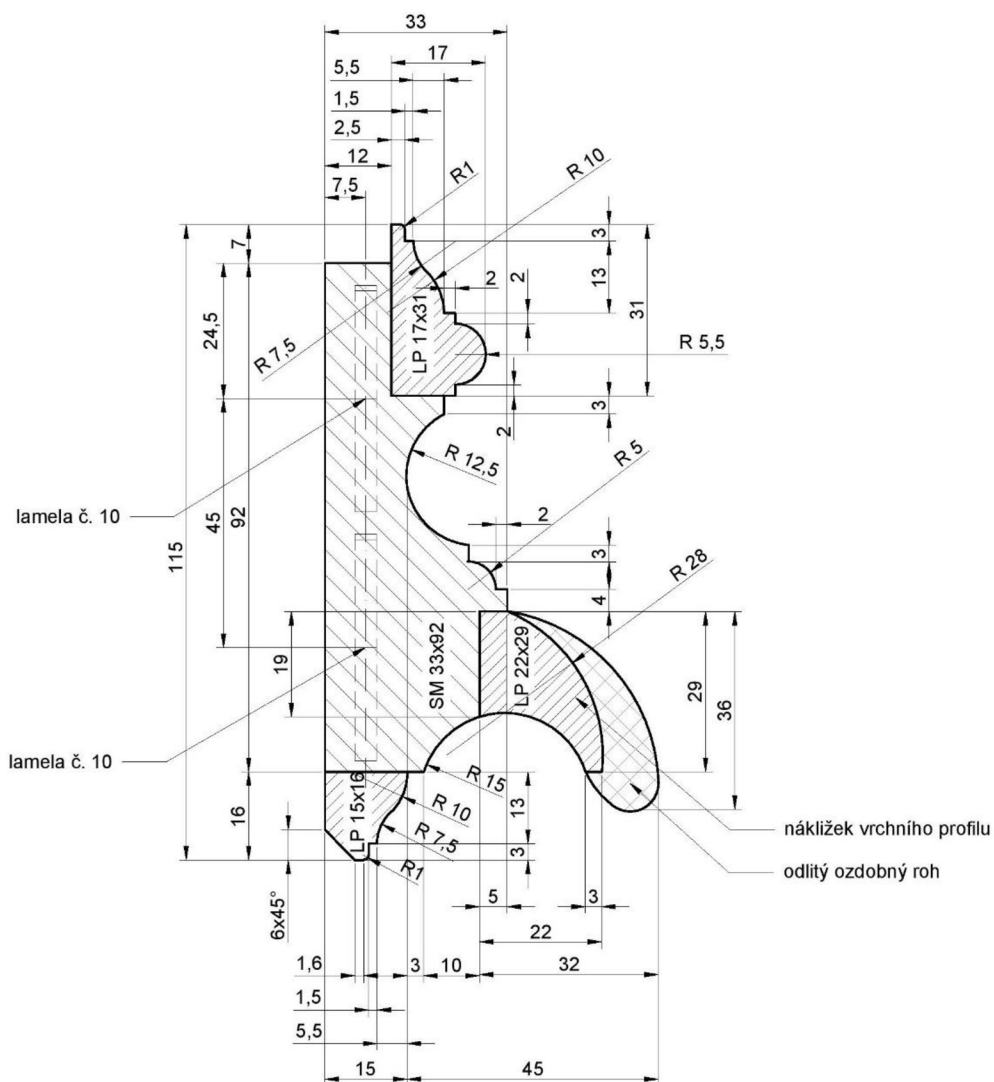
Popis ornamentů rámu a technik jejich zhotovení
